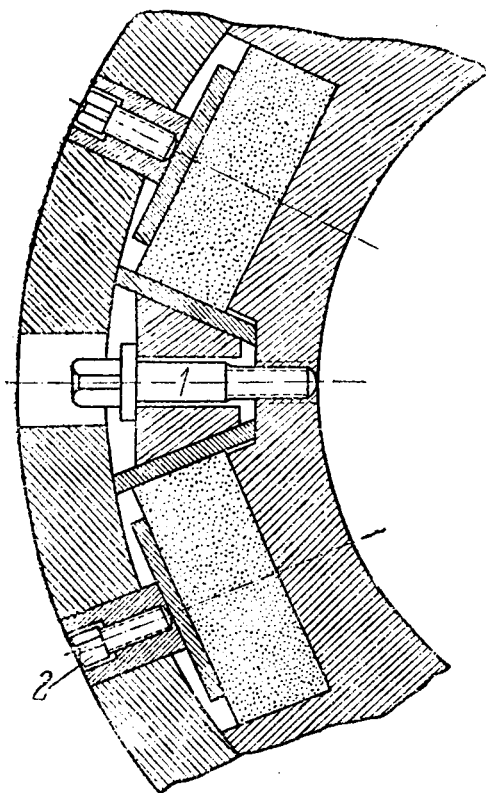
Патрон для зажима сегментов станка МСЗ, тип 3732
